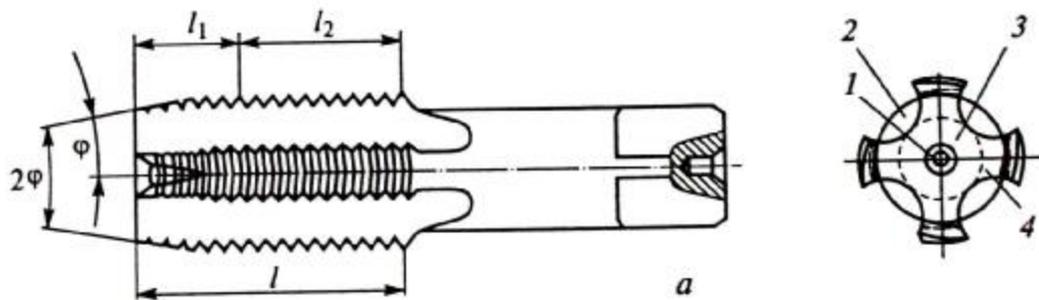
Метчик для нарезания внутренней резьбы: 1 – центровое отверстие; 2 – канавки; 3 – сердцевина; 4 – зуб
